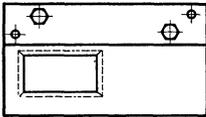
Einseitige Querrführung für sperrige Werkstücke.
